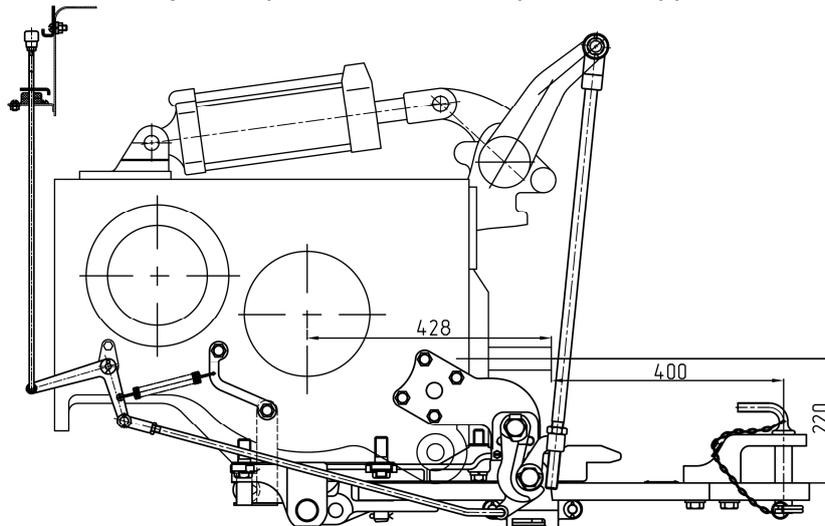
Schéma d'installation du dispositif TSU-1M-02 (avec le pendule installé dans la position de fonctionnement et le crochet hydraulique installé dans la position supplémentaire)
